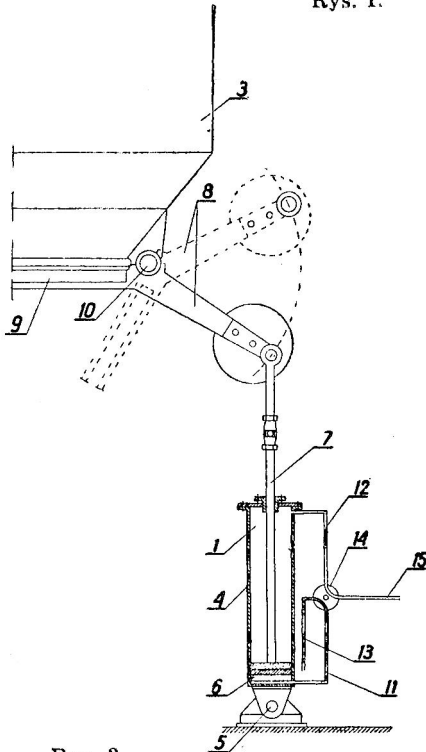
przedstawia zainstalowanie przyrządu 1 pod podestem 2 przy dyfuzorze 3, rys. 2 — szczegóły konstrukcji tego przyrządu, rys. 3 — konstrukcję zaworu czwór-droźnego w przekroju pionowym, a rys. 4
